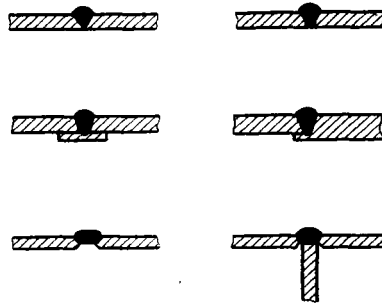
Соединения при сварке в среде защитных газов
